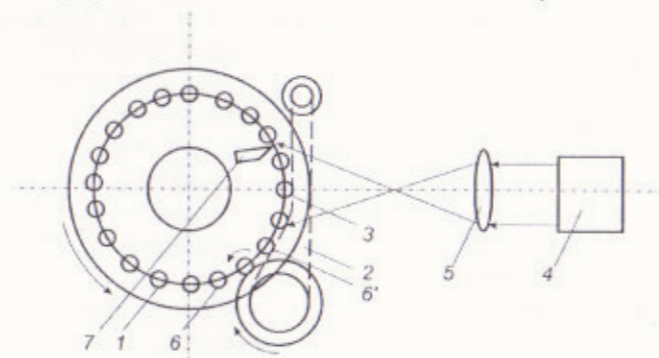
Кинематическая схема установки резки колец для плоской ножки ЭОС
